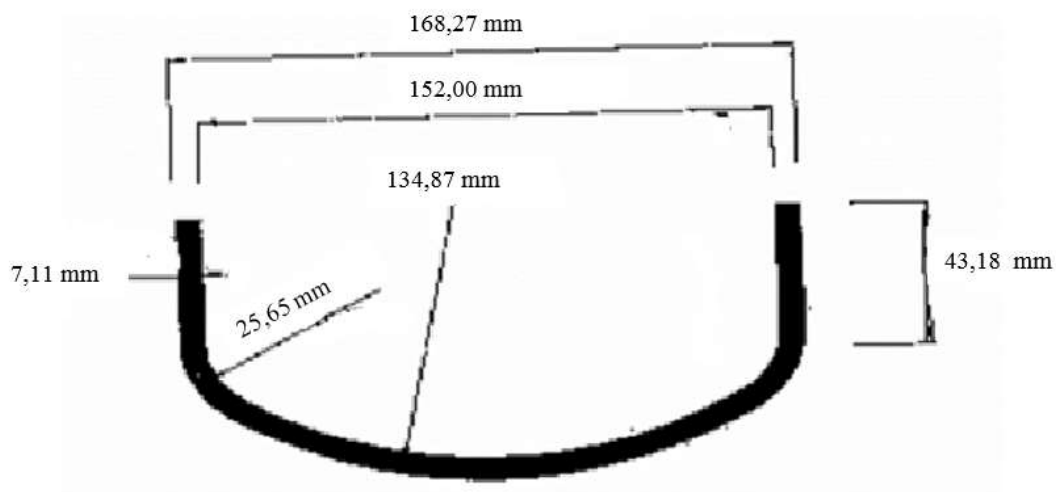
Cápsula de soldar de 152 mm y 2.90 kg.
